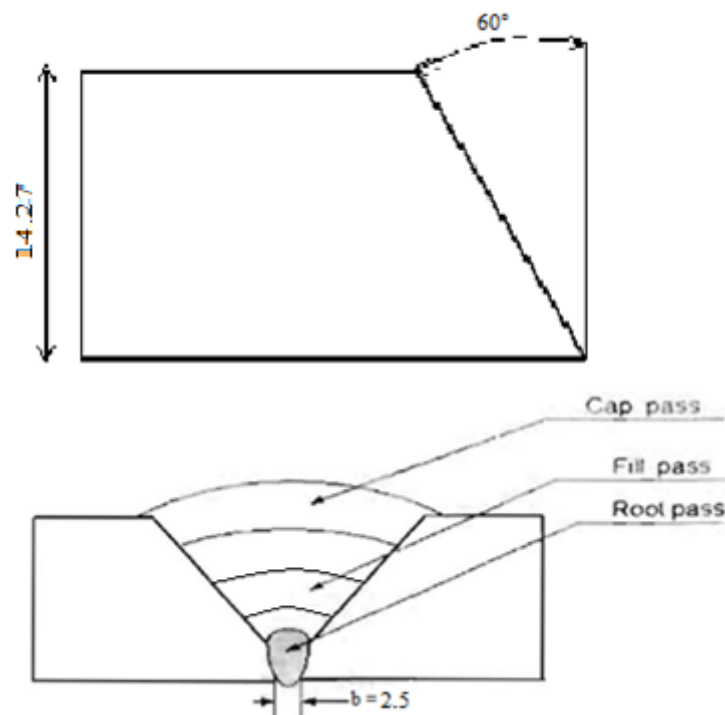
Forme du joint de soudure et le nombre de passe.
